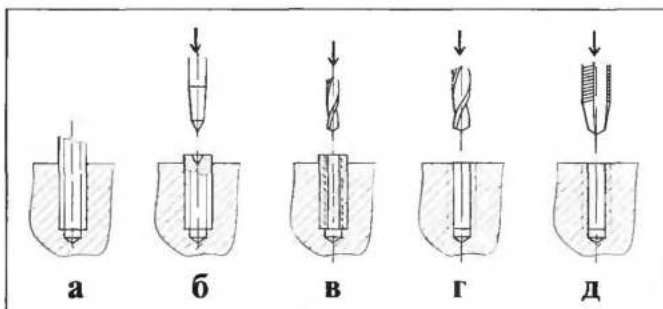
Стандартная схема высверливания обломанной шпильки (болта):
